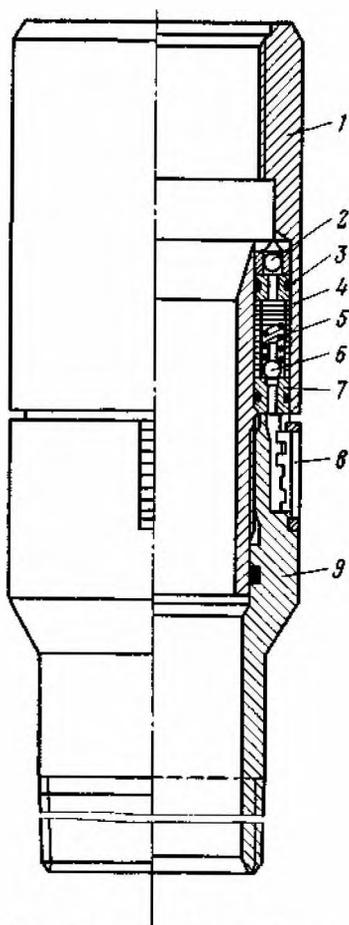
Ингибиторный клапан типа КИНГ:
